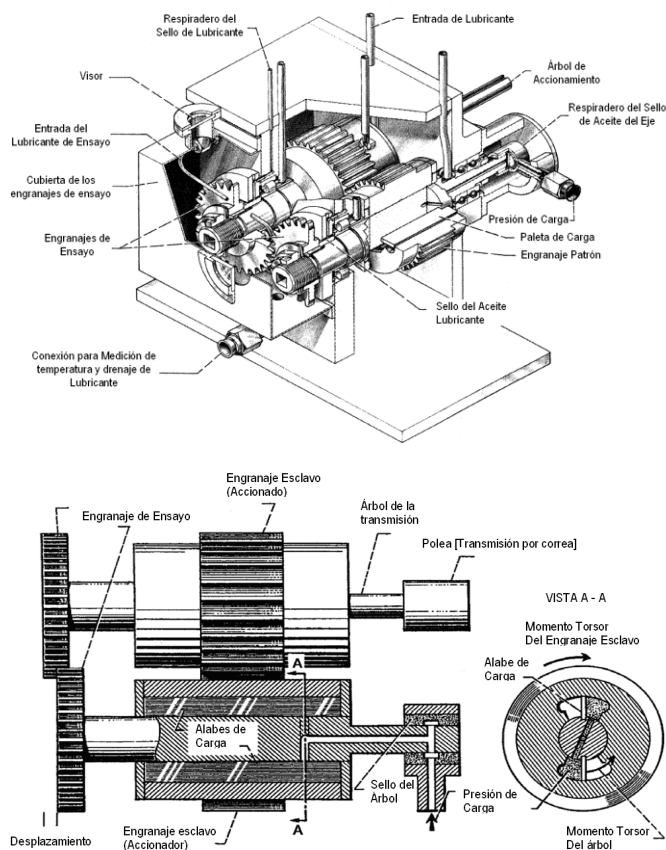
Máquina para ensayo de engranajes NASA [49].
